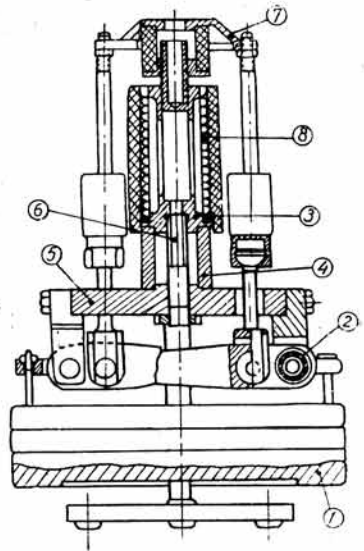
Установка для припикання у вакуумі: 1 — знімні вантажі; 2 — шарикопідшипникова опора; 3 — гніздо для укладення зразків; 4 — керамічна труба; 5 — установочна плита; 6 — порожнистий гвинт; 7 — навантажуюча траверса; 8 — піч опору.
